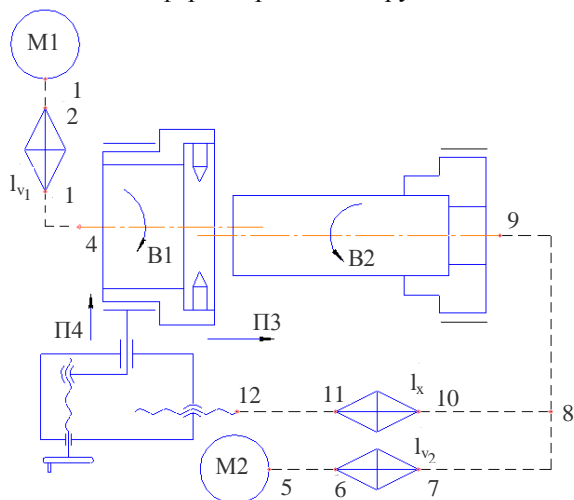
Структурная схема станка для обработки круговых винтовых поверхностей резцовой головкой
